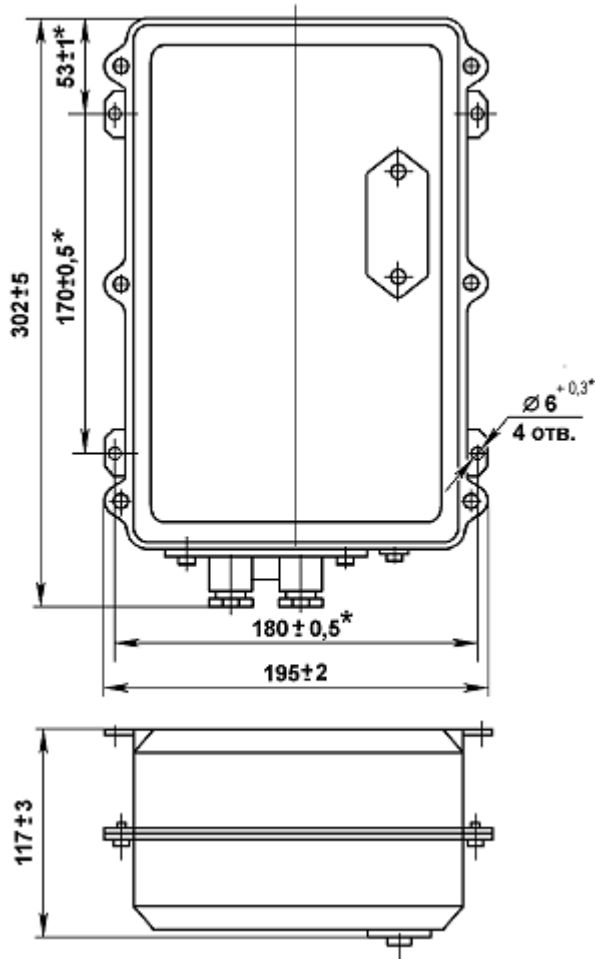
для усилителей ФЦ-0610, ФЦ-0611
